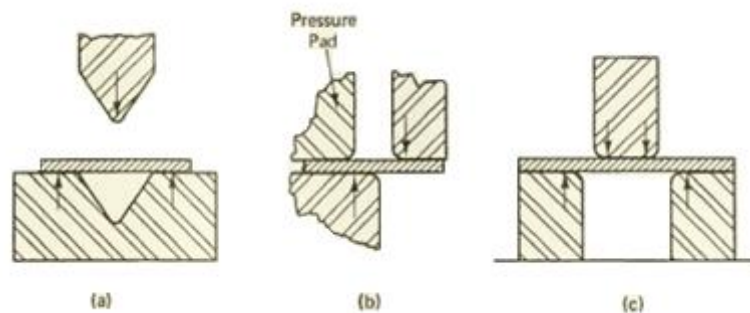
Tipos de dobragem: (a) Molde em V; (b) Molde simples; e (c) Molde em U
